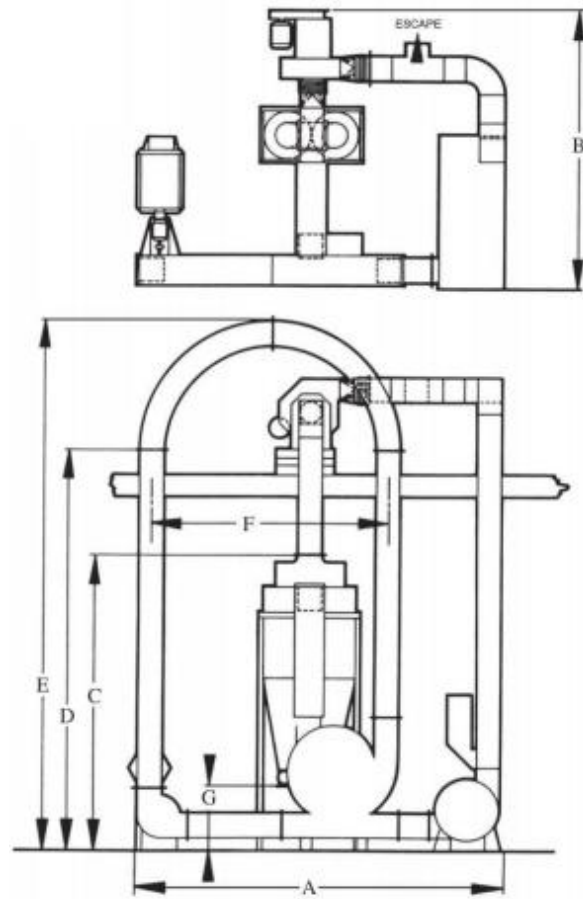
Dimensiones de Secador de anillos. Fuente: Dupps.
